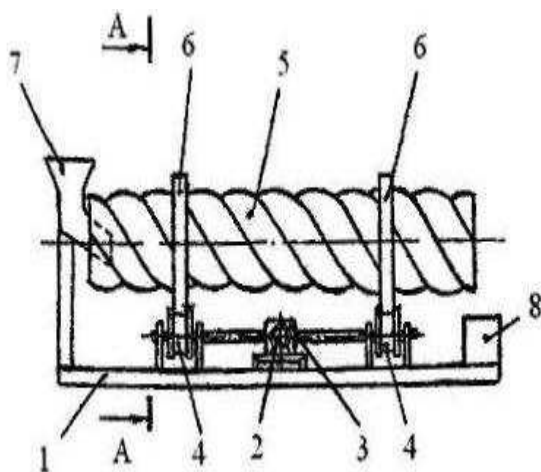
Барабанный смеситель сыпучих материалов, вид спереди
